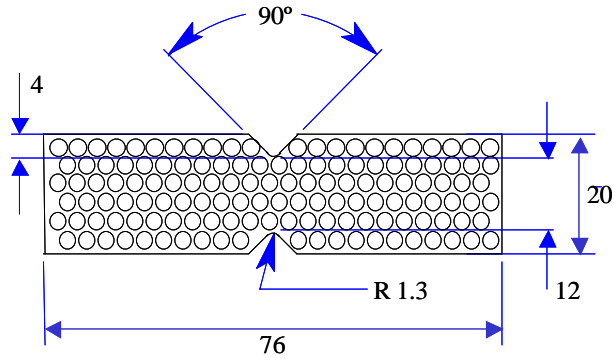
Esquema de la probeta del ensayo Iosipescu.
